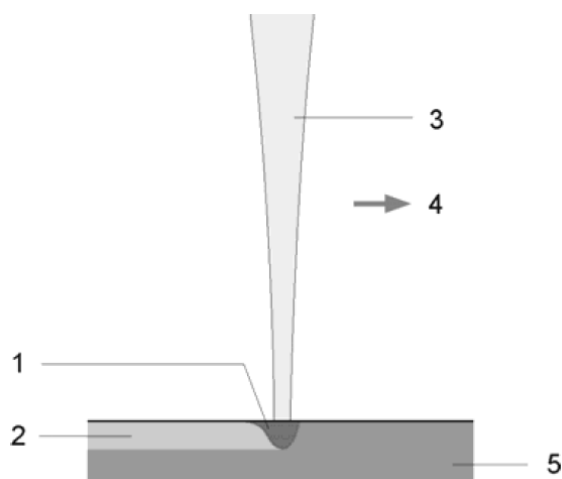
Representação esquemática dos diferentes tipos de soldadura [22]
